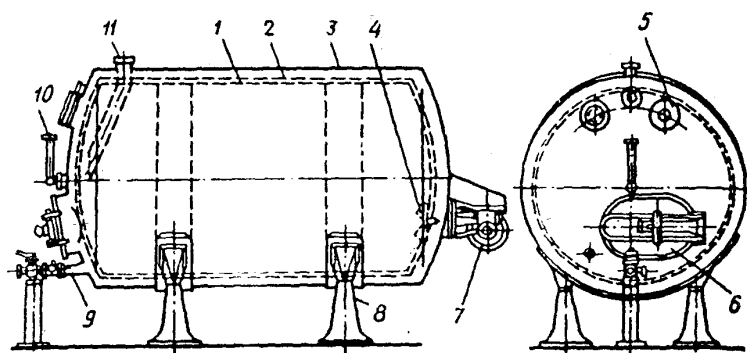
Горизонтальний резервуар для зберігання молока: 1 – робітник резервуар; 2 – теплоізоляція; 3 – кожух; 4 – мішалка; 5 – оглядове вікно; 6 – люк; 7 – привод мішалки; 8 – опорні ніжки; 9 – зливальний патрубок; 10 – термометр; 11 – наливна труба
